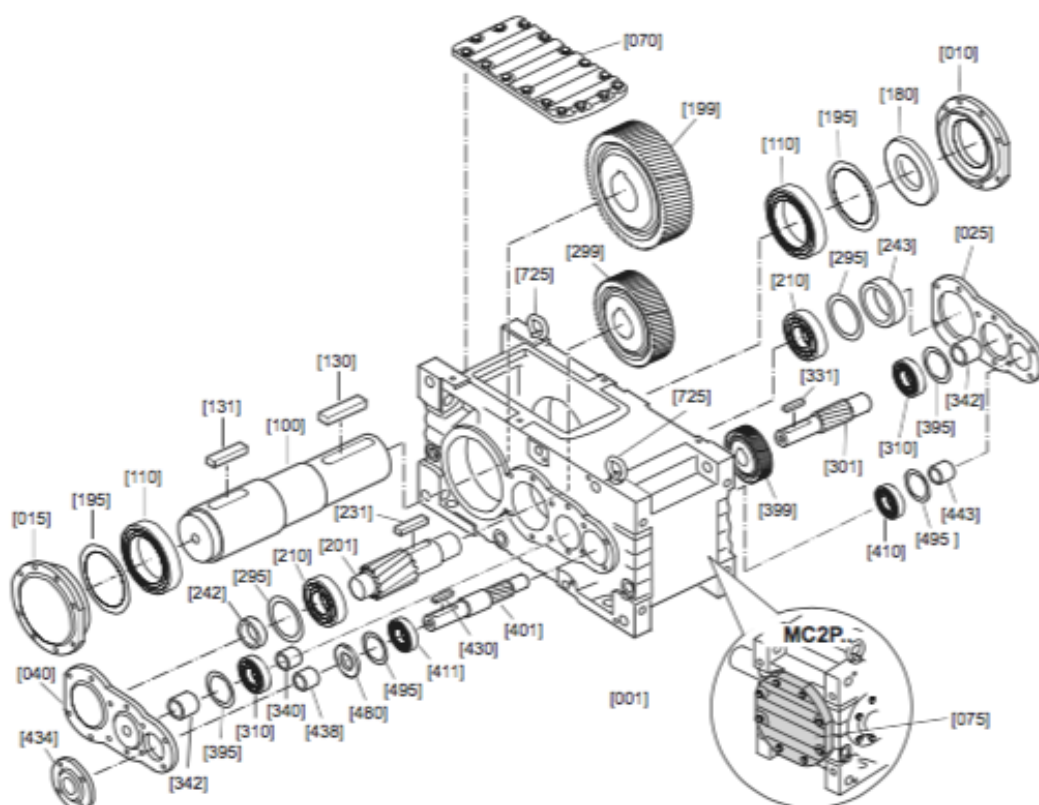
Desenhos 2D do redutor de engrenagens MC2PLSF04.
